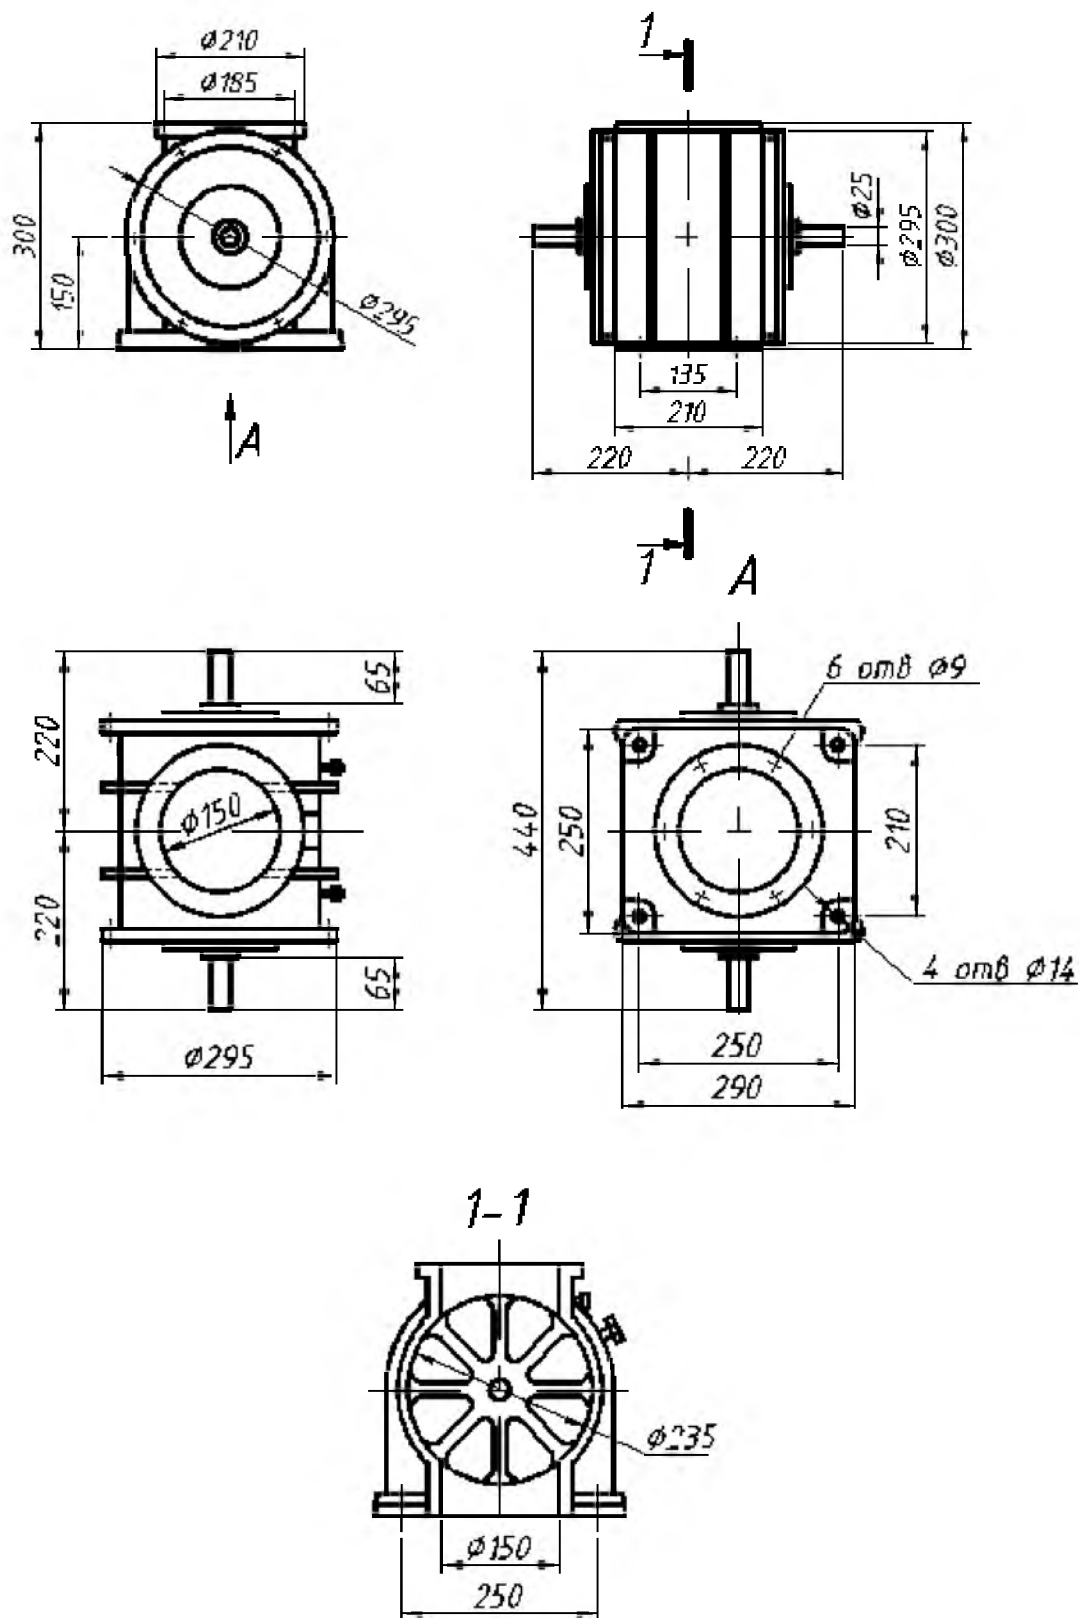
Шлюзовой затвор Шу-6
